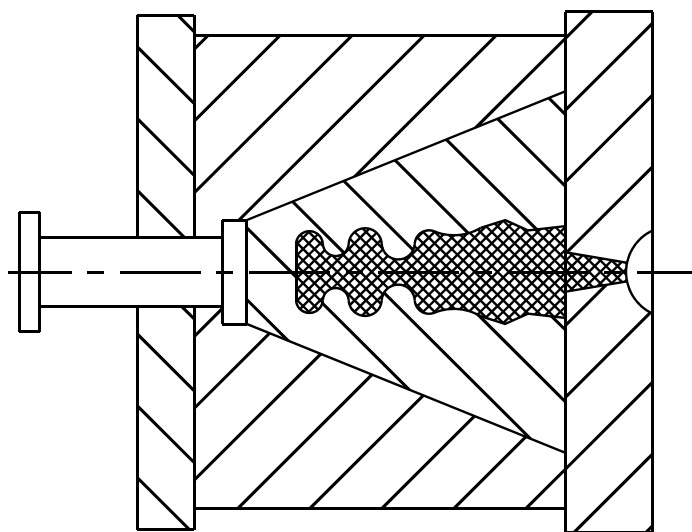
Схема пресс-формы с раздвижными полуматрицами
